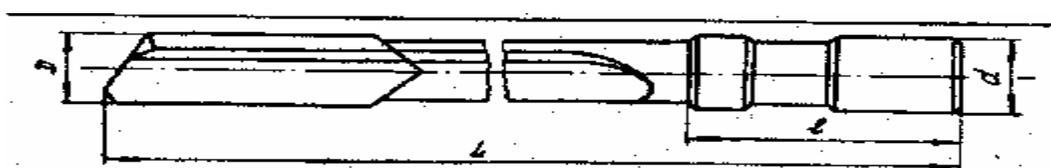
Сверла одностороннего резания для глубокого сверления по ТУ 2-035-655-79
